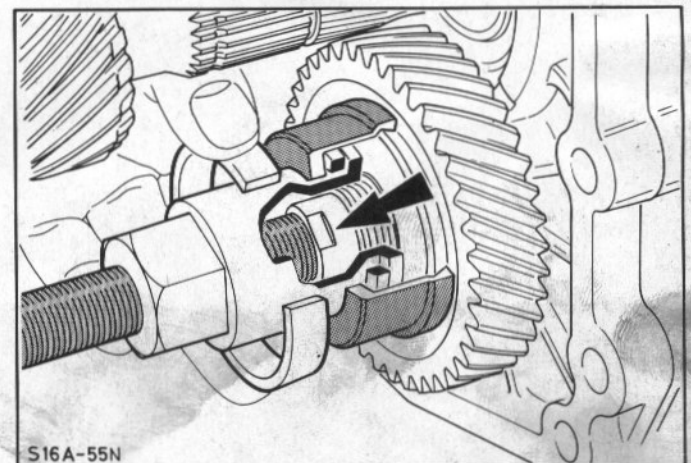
Spezialwerkzeug an Zahnrad-5. Gang anbringen
